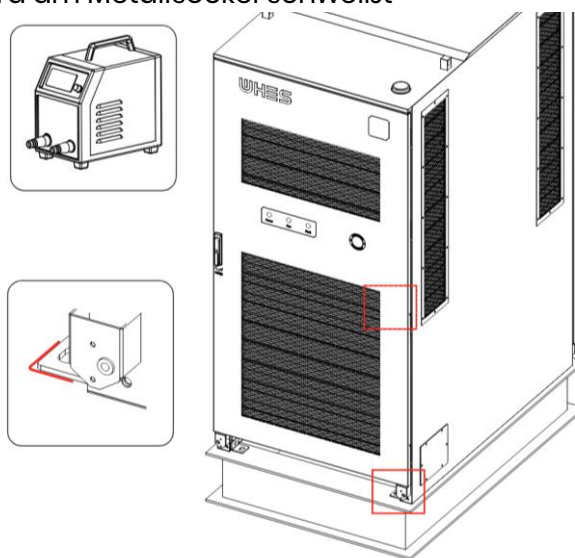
Es wird am Metallsockel geschweißt
